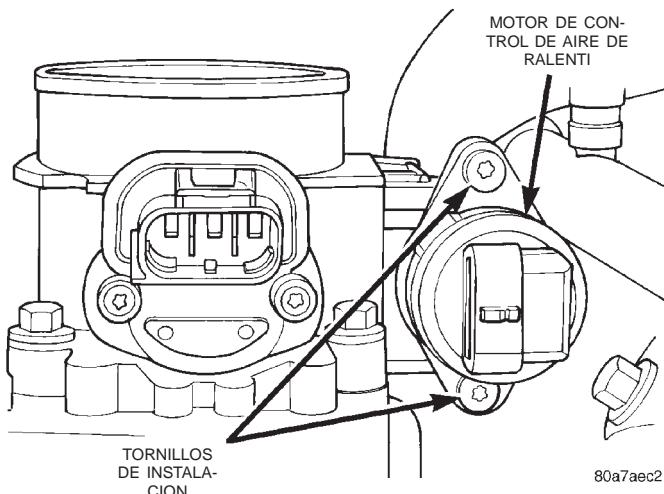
Pernos de instalación (tornillos)—Motor de IAC
